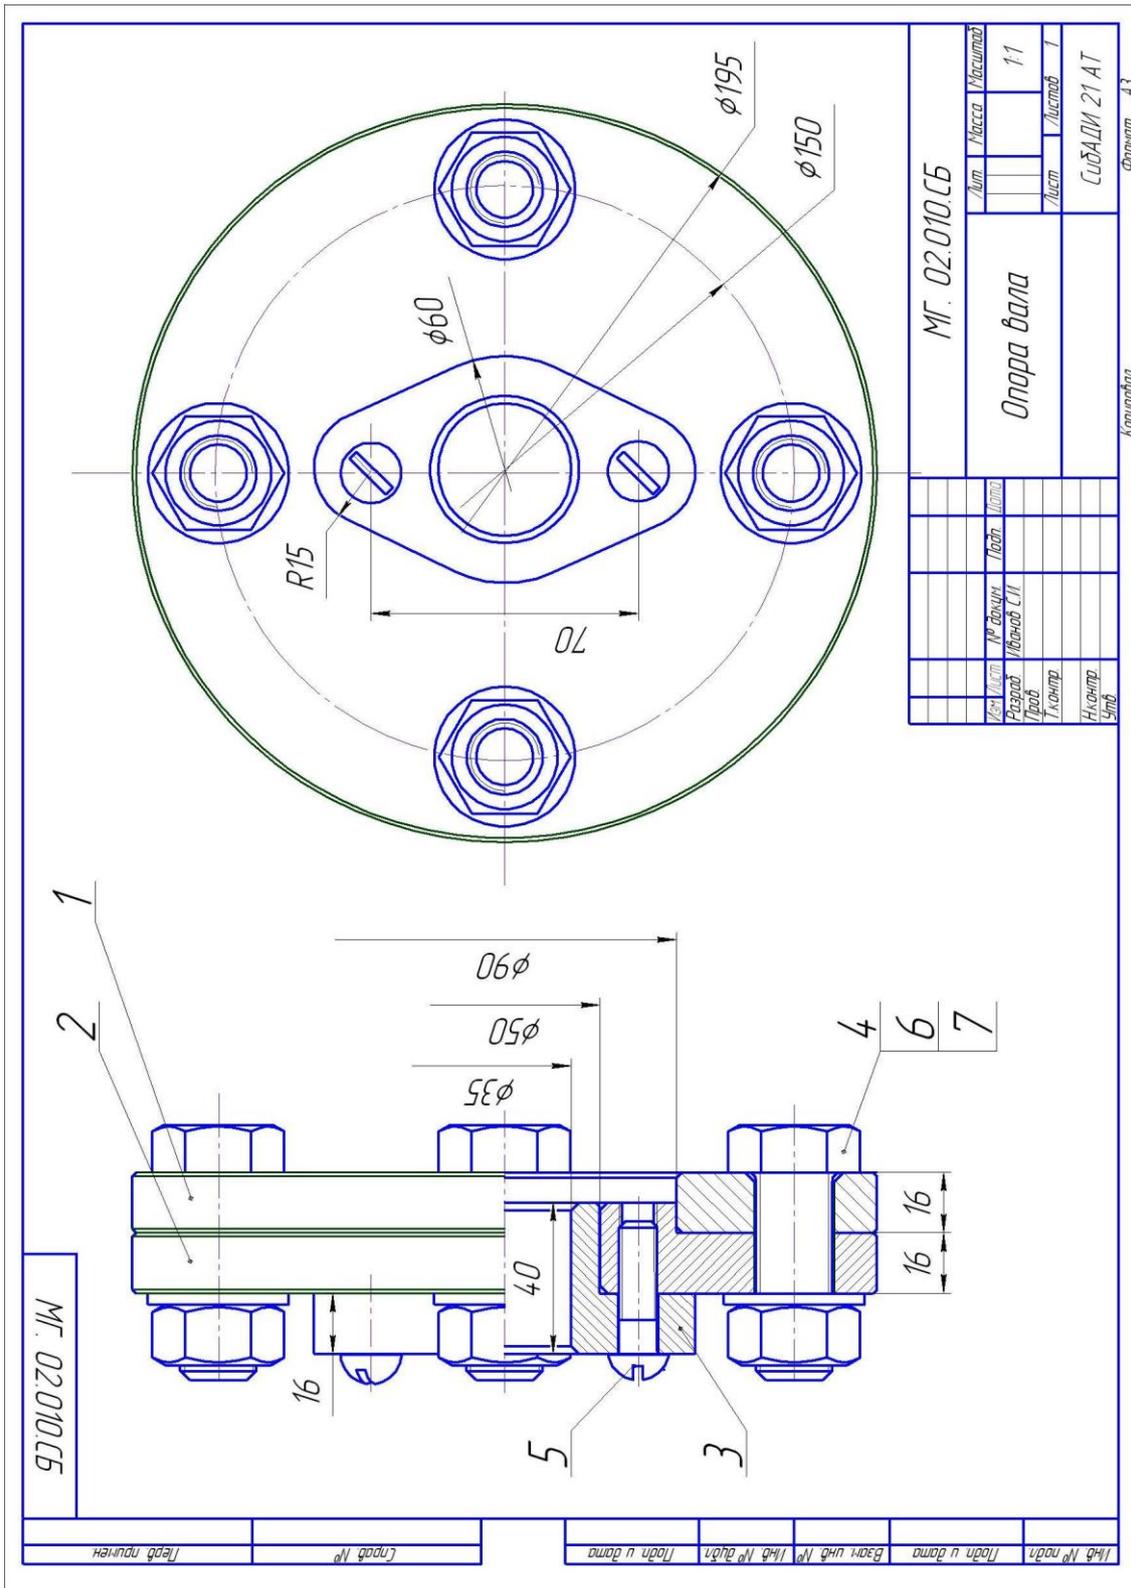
Сборочный чертёж «Опора вала» – исходные данные для выполнения сборки узла машиностроительной конструкции
